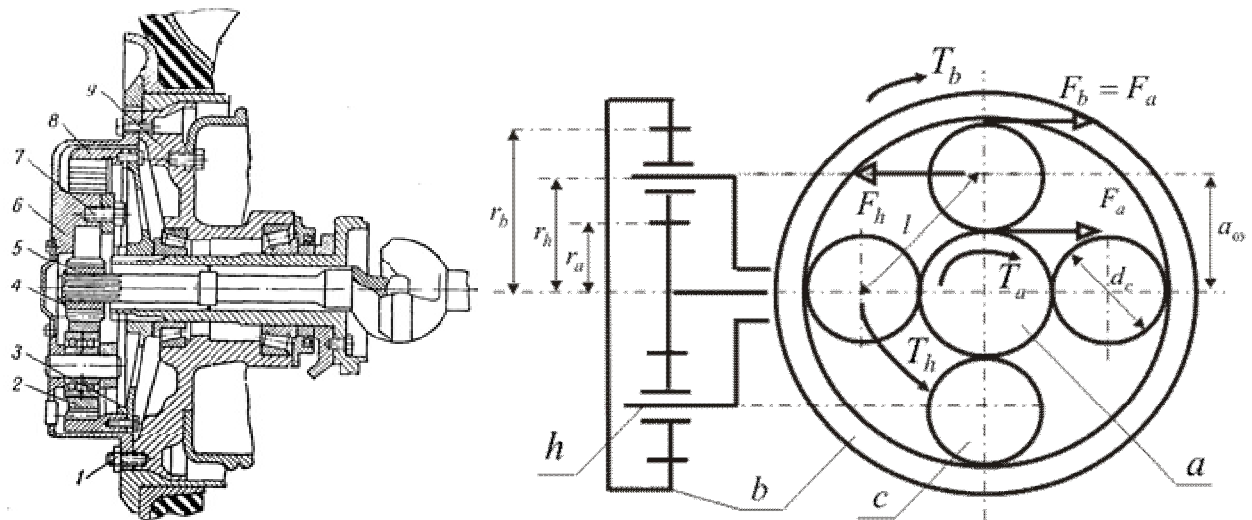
Планетарний колісний редуктор із заблокованим епіциклом:
